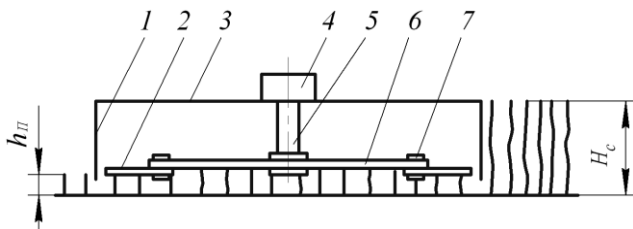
Схема різального апарату подрібнювача-розподільовача з дисковим робочим органом: 1-обичайка; 2-ніж; 3-кожух; 4-редуктор; 5-вал; 6-тримач; 7-шарнір
